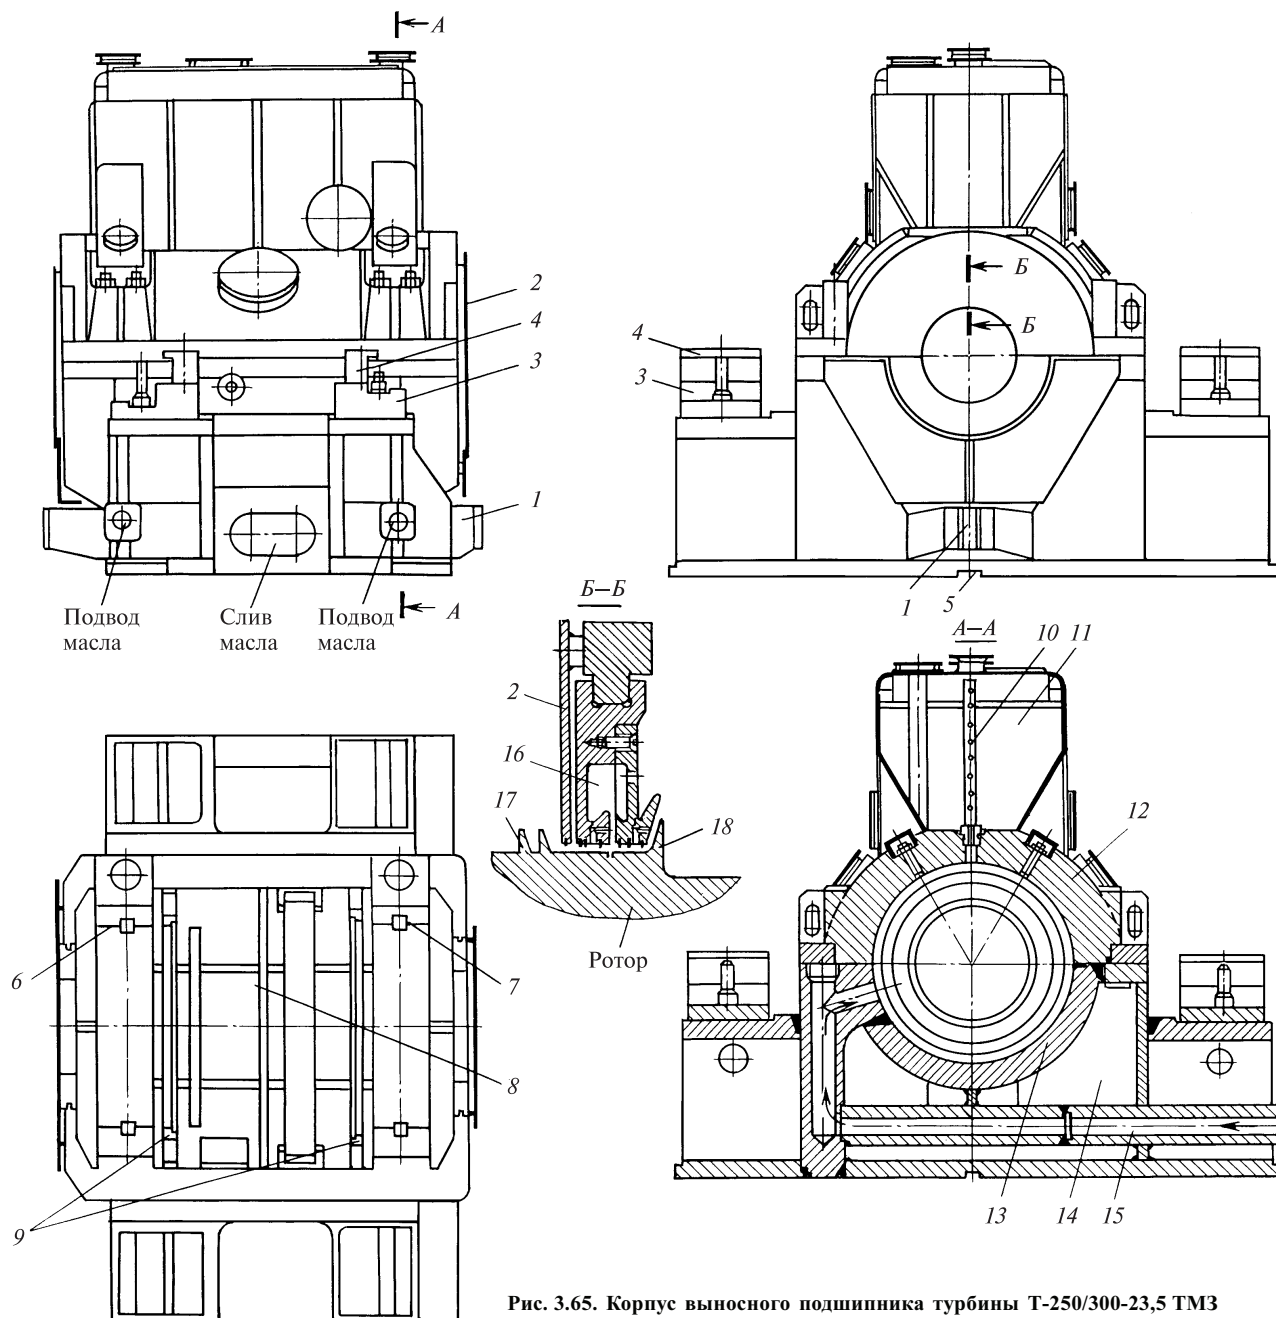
Корпус выносного подшипника турбины Т-250/300-23,5 ТМЗ
